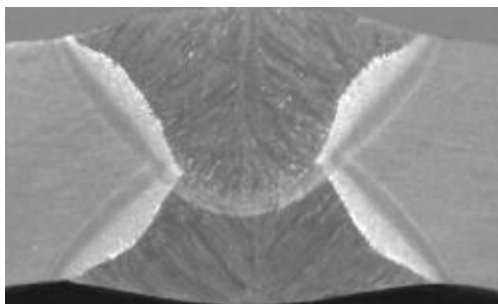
Φ1 016 mm×17.5 mm 焊管焊缝宏观形貌
